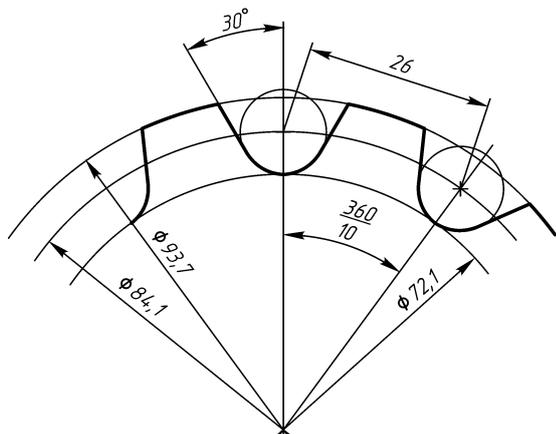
Профиль зубьев и размеры ведомого колеса волновой зубчатой передачи с невращающейся втулочно-роликовой цепью
